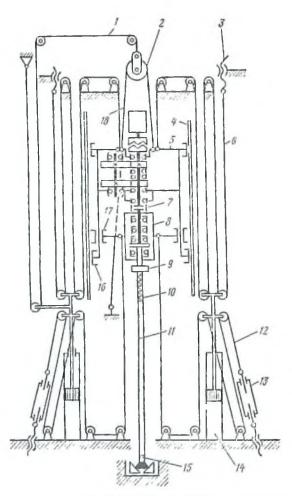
1. Кинематическая ехема вращательно-подающего механизма шлиндельного типа с канатно-поршиевой лодачей стапка шарошечного бурения СБШ-250MHA-32
